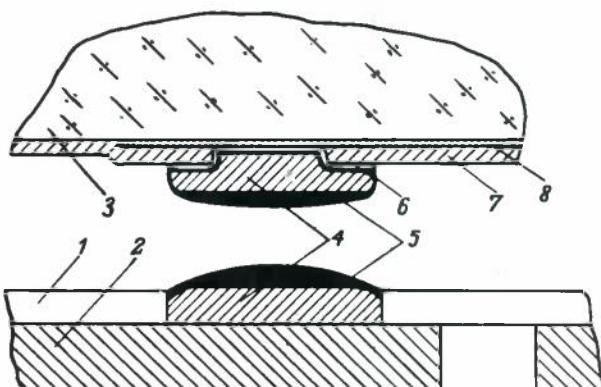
Контактный узел кристалл–гибкая плата: 1 – полимид; 2 – медная фольга; 3 – кристалл; 4 – гальваническая медь; 5 – припой; 6 – барьерно-адгезионный слой; 7 – защитное покрытие; 8 – алюминиевая разводка
